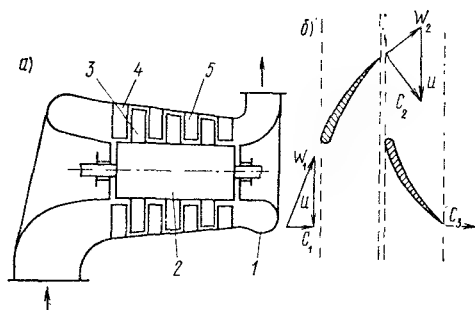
Схема осевого компрессора (а) и профиль рабочих и спрямляющих лопаток (б)
